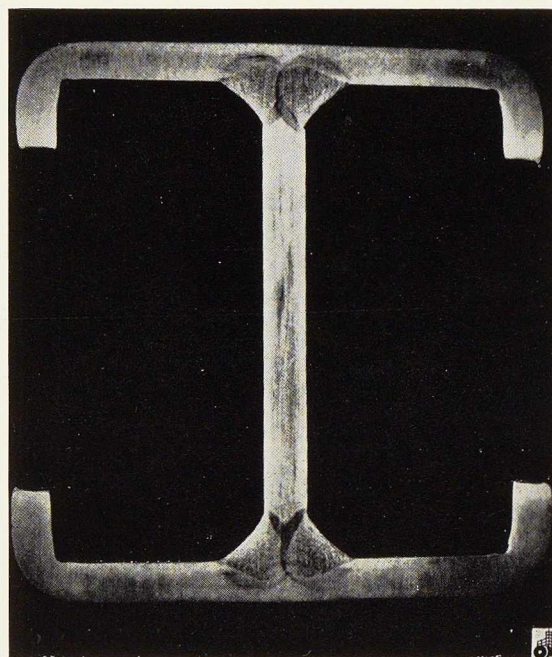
Macrographie de soudure exécutée par le procédé Unionmelt.
